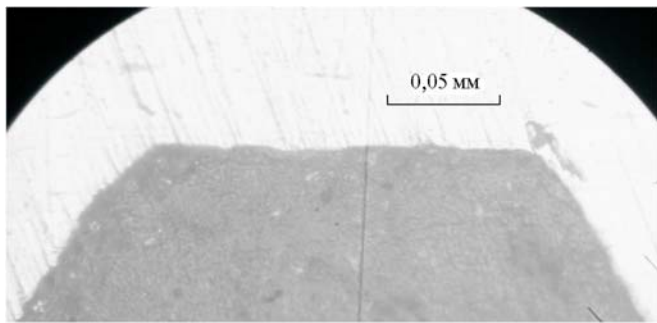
Фотография профиля дна впадины наружной резьбы М12, обработанной резьбовой фрезой
